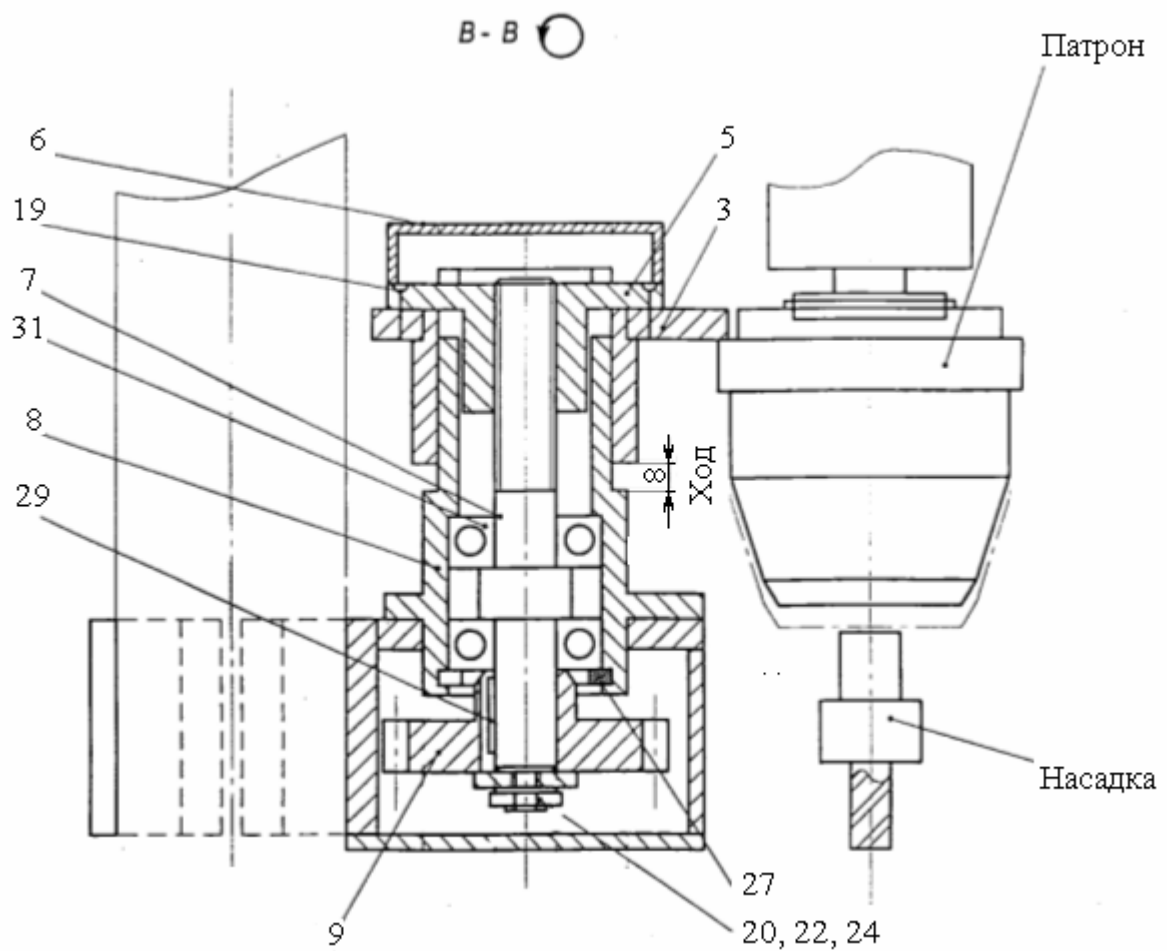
Разжимной механизм (компоновка на станке и разрез)
